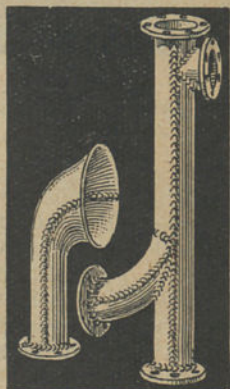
Tubagem de cobre feita pela soldadura autogenea.
